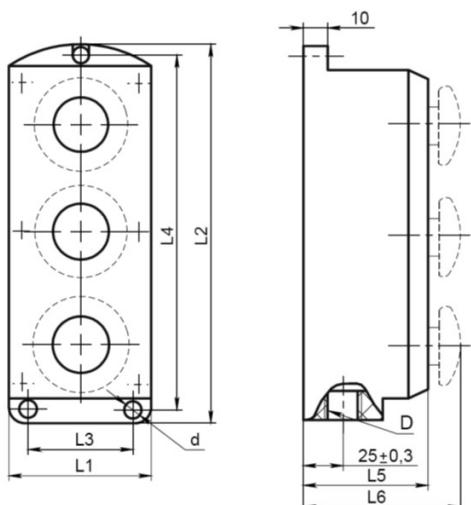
Габаритные и установочные размеры постов ПКЕ для установки на ровную поверхность
